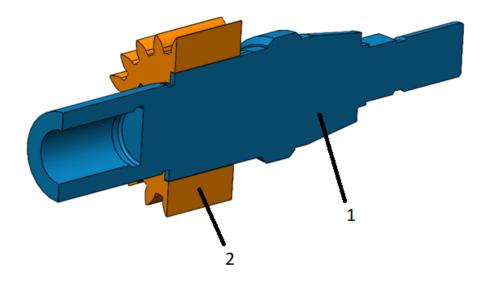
Вид с разрезом: 1 – вал, 2 – зубчатое колесо.
